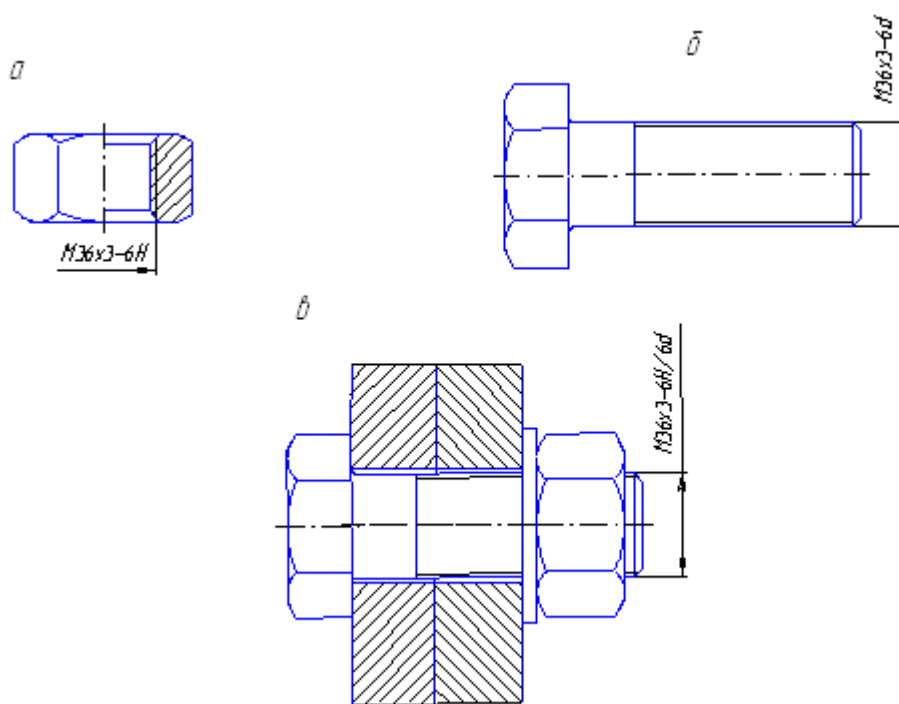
Условные чертежи: а – гайка; б – болт; в – резьбовое соединение
